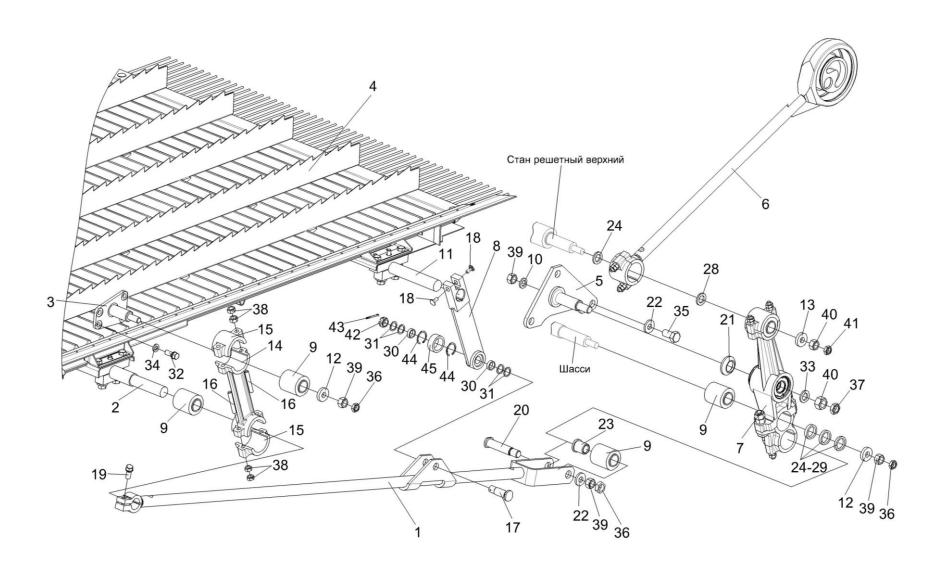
Установка привода доски стрясной КЗК 0280000А (вид слева)
